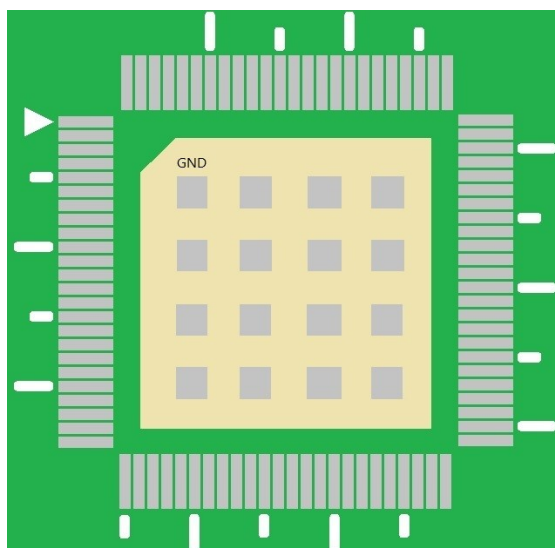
：LT779C 底部焊盘 PCB 的设计建议-1
